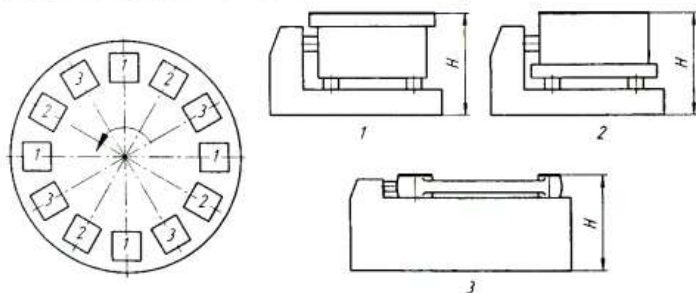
Пристрій для одночасного групового оброблення на карусельно-фрезерному верстаті
